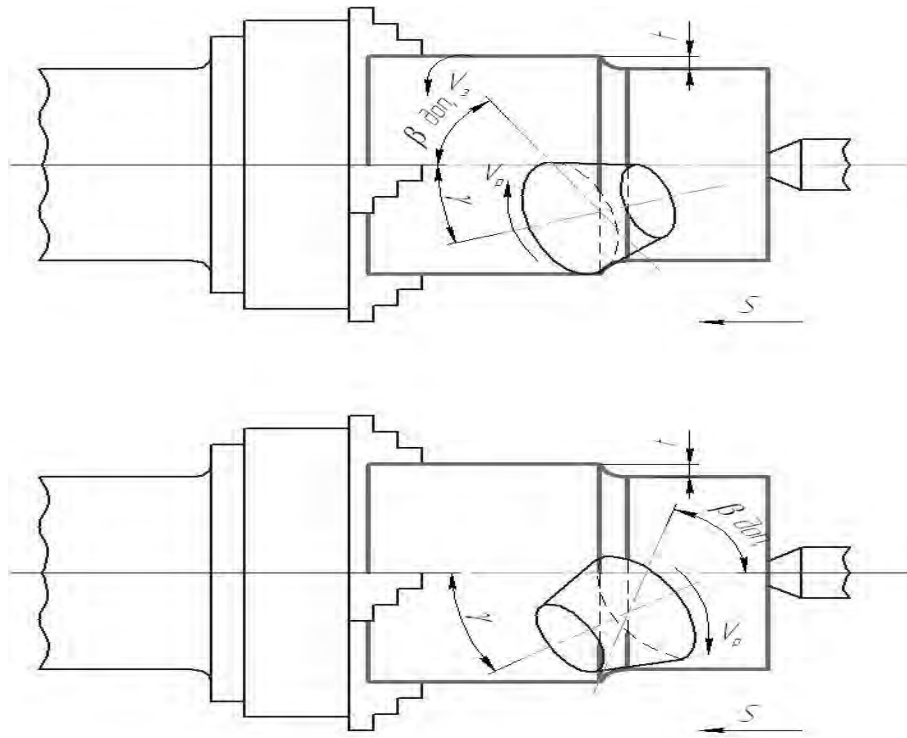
Схемы установки чашечного резца ниже оси обрабатываемой заготовки
